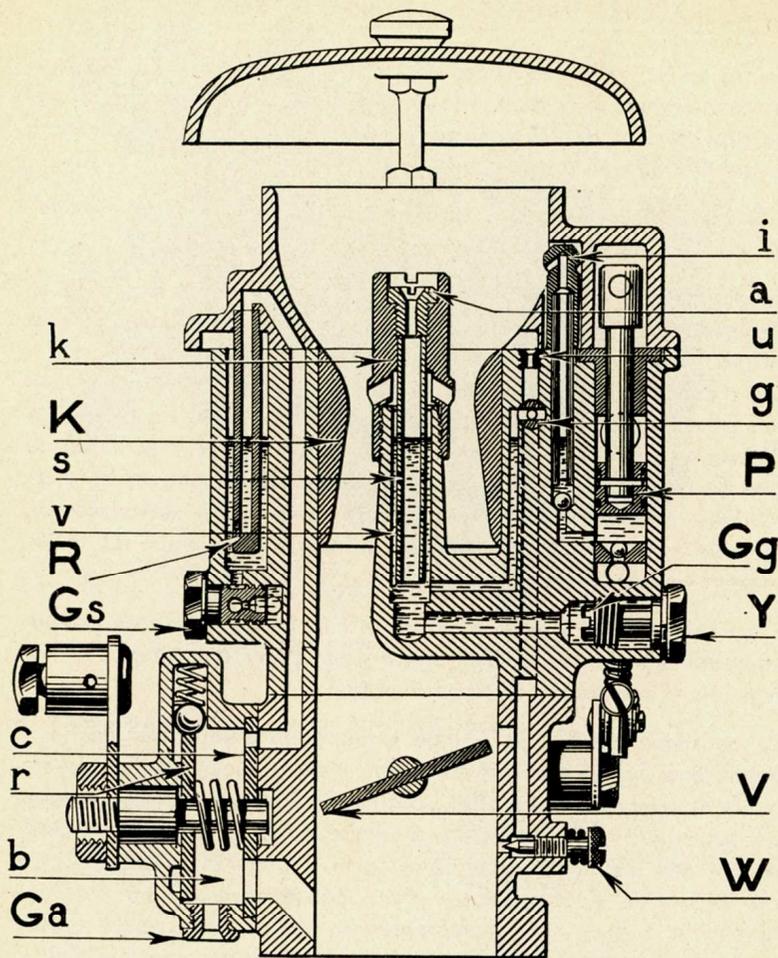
Coupe du carburateur inversé à pompe (montage 20).
